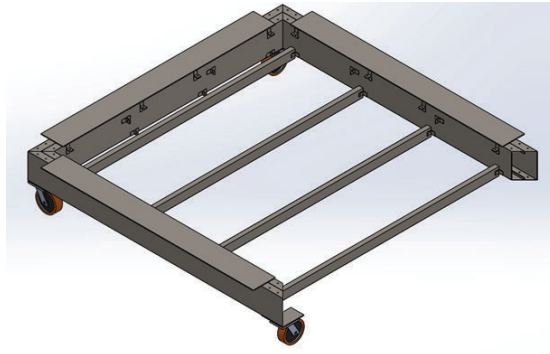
Inicio del ensamblaje de la estructura (Fuente propia)
